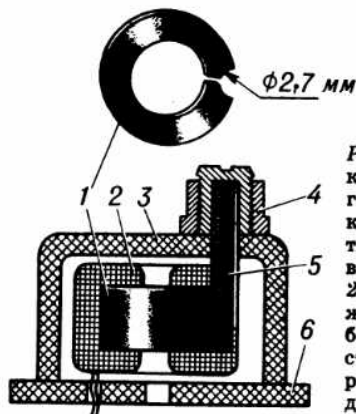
Конструкция катушки низкочастотного контура с регулируемой величины индуктивности: 1 — ферритовое кольцо с вырезом; 2 — обмотка; 3 — кожух; 4 — фланец с резьбой; 5 — ферритовый стержень (вклеен в резьбовую пробку); 6 — дно кожуха.
